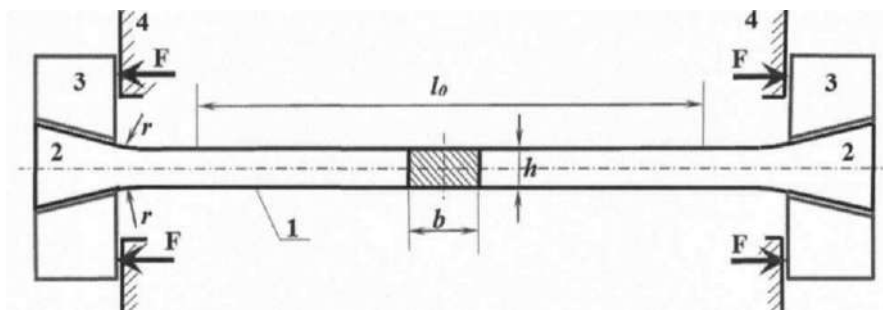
Зразок для випробування композитів на розтяг: 1 – базова частина зразка завдовжки l_0 , 2 – заплечики у формі клина, 3 – вилки захоплення, 4 – контактна поверхня захватів
